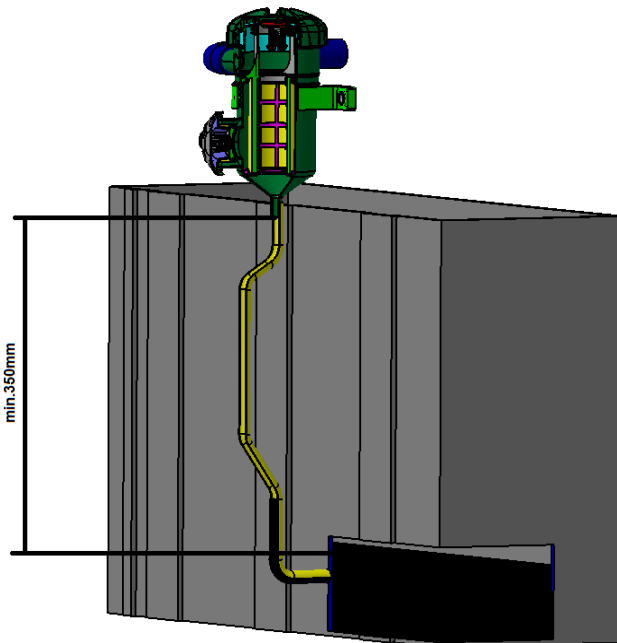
Ecartement minimum du niveau d'huile par rapport au conduit de retour d'huile
